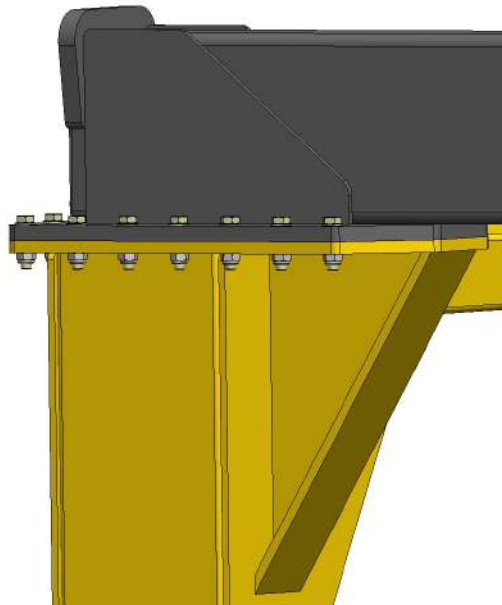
Nudo viga telescópica – columna: placa de unión atornillada y rigidizadores de refuerzo en la cabeza de la columna.
